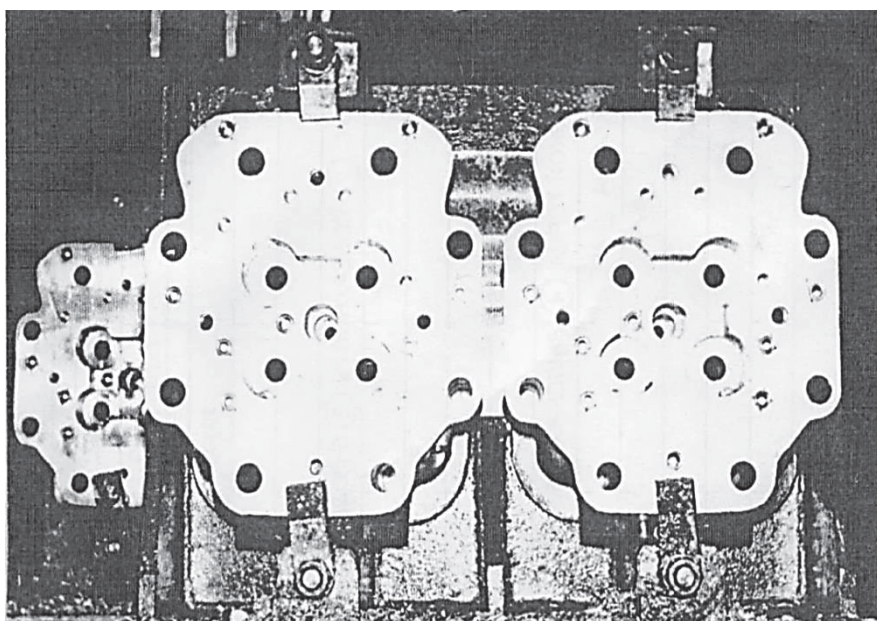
Заготовки детали «Головка блока цилиндров» на паллете-спутнике при обработке
